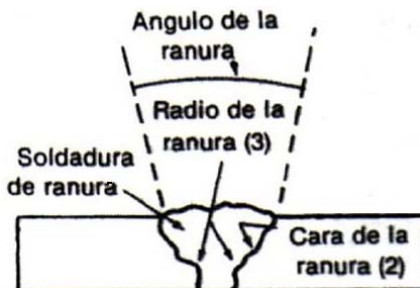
Soldadura de ranura en corte transversal
